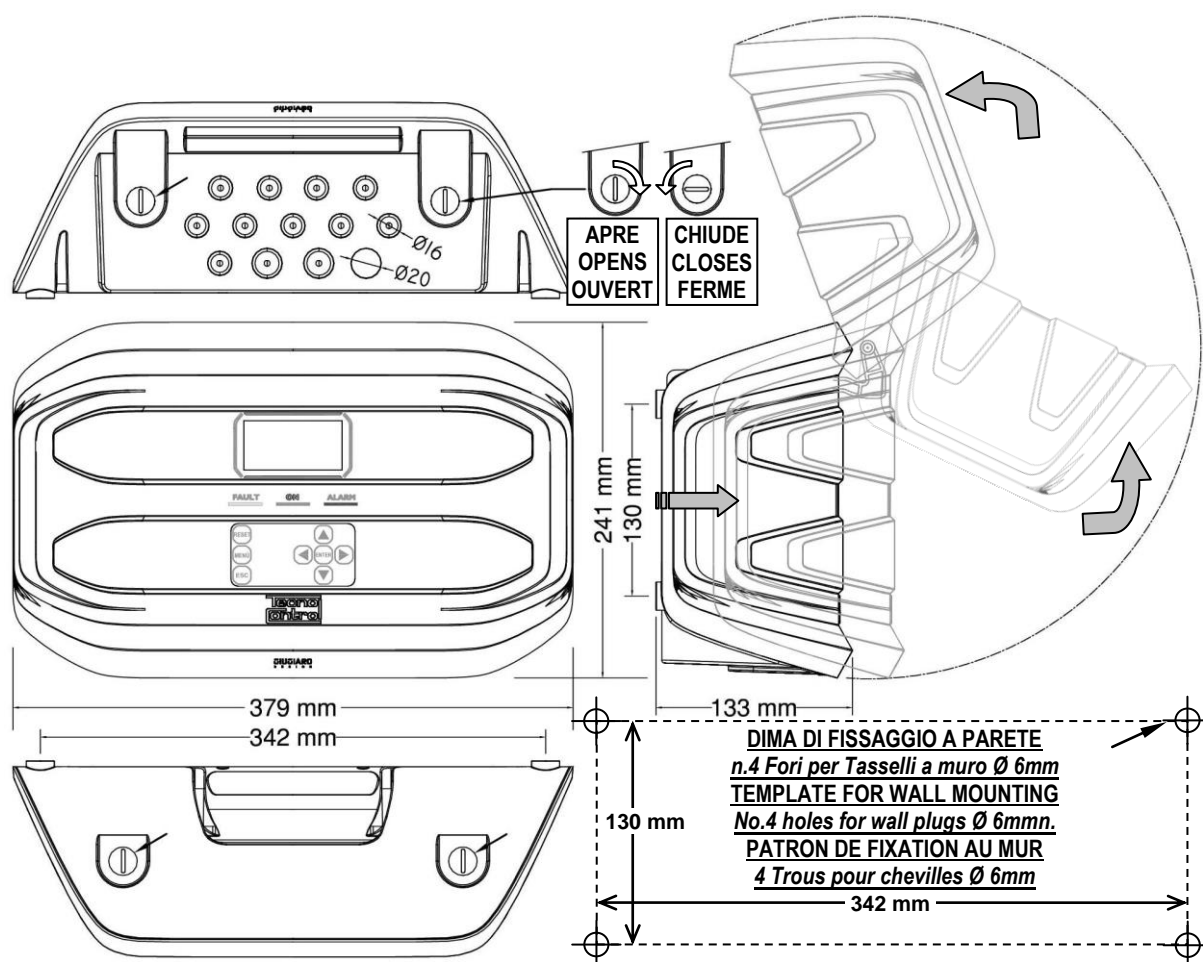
CE516P Dimensioni e Dima di Fissaggio.
